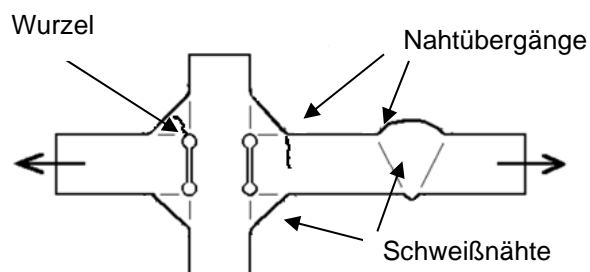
Schweißnahtversagen am Kreuzstoß
